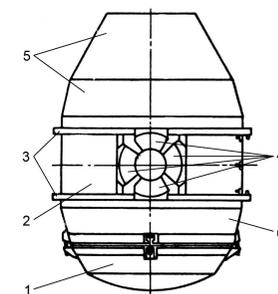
Конструкция корпуса конвертера для МК им. Ильича:
